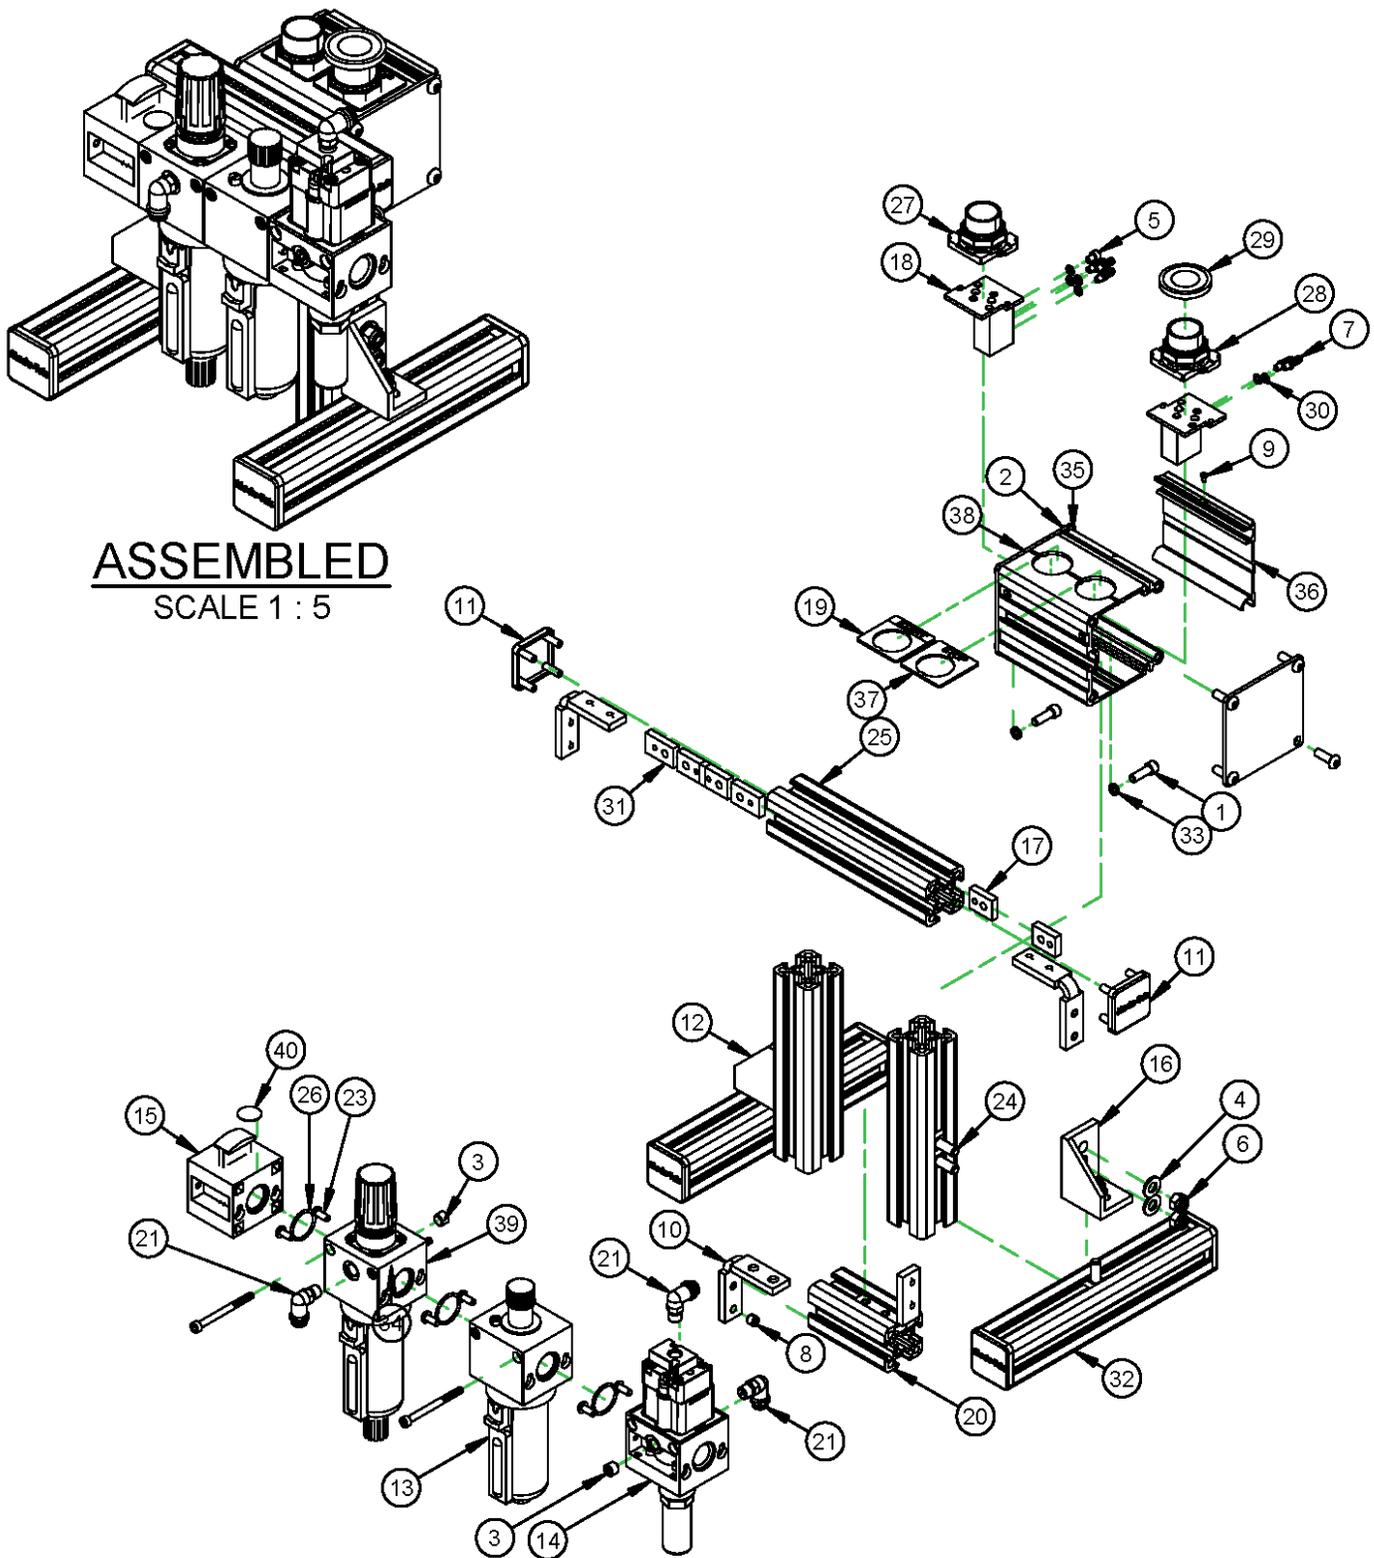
MONTAJE DE LA UNIDAD DE ACONDICIONAMIENTO NEUMÁTICO (N/P 78264)
